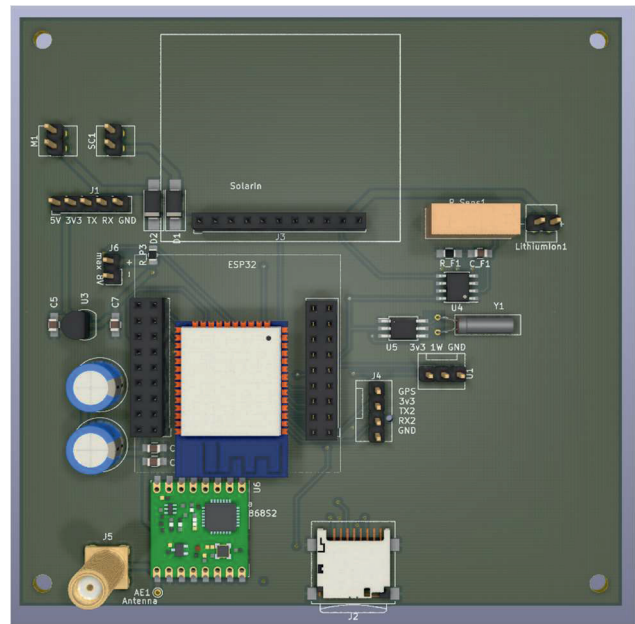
Gerenderte Darstellung des PCB Prototypen
